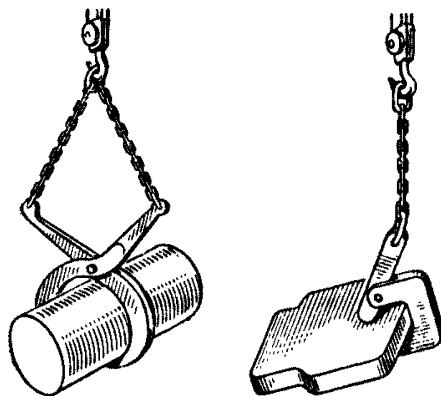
Строповка отливок за цапфы, рамы и скобы
